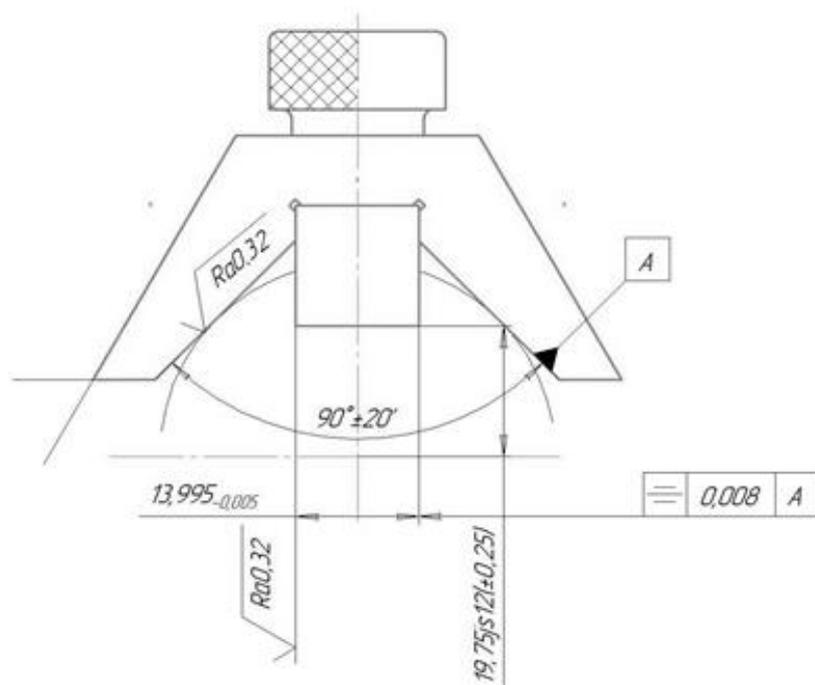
Эскиз калибр-призмы для контроля ширины паза шпонки на валу 14H9
